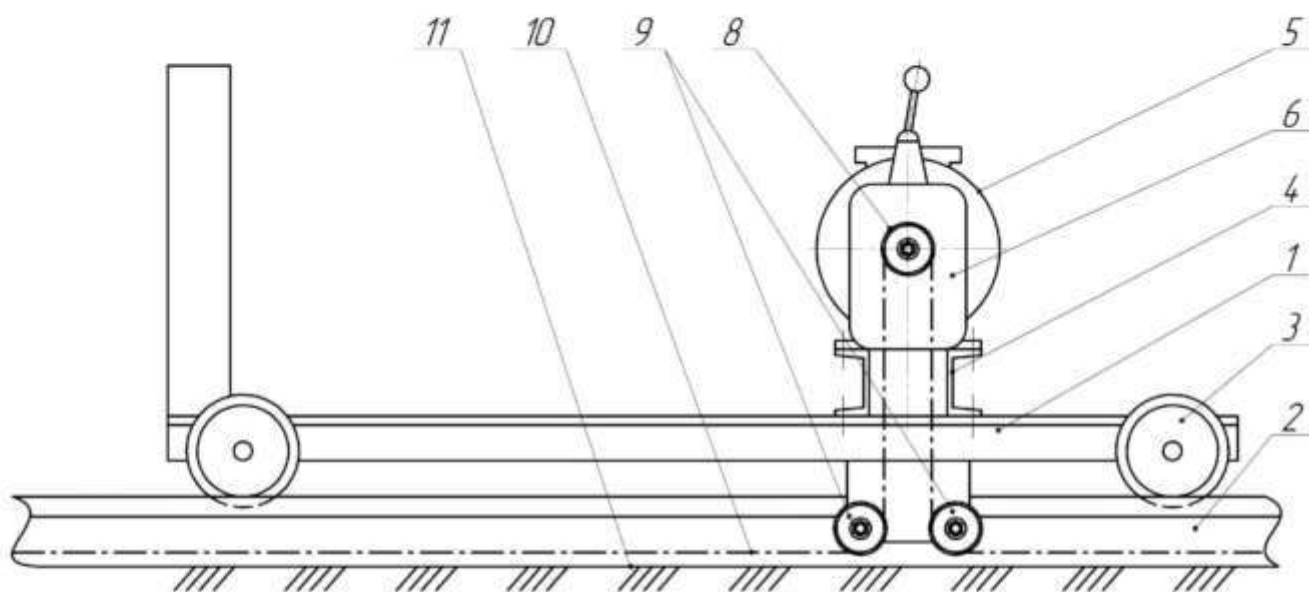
Общее устройство подвижного модуля с приводом от цепной передачи
